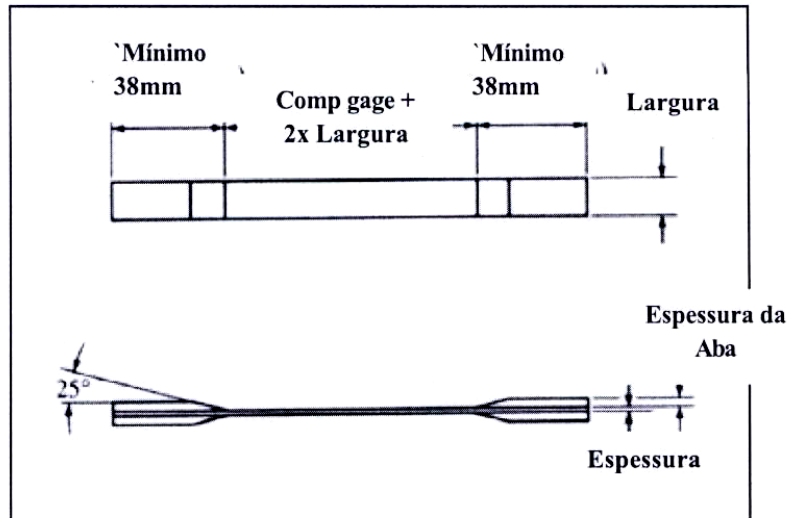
Dimensões dos corpos-de-prova para ensaio de tração; ASTM D 3039.
